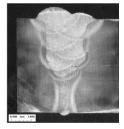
Микрошлиф лазерно-дуговой сварки
